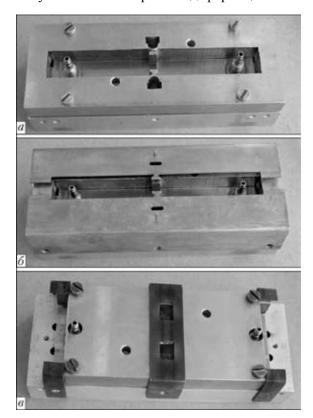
Сборочно-сварочное приспособление для электроннолучевой сварки измерительной камеры (×1,67): a — сборка без защитных экранов; δ — сборка с защитными экранами для выполнения нахлесточных швов соответственно вдоль длинной и короткой (ϵ) сторон
